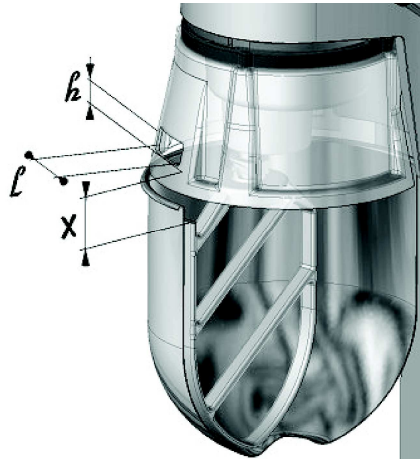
Planetenrühr- und -knetmaschinen mit einer geschlossenen Abdeckung
